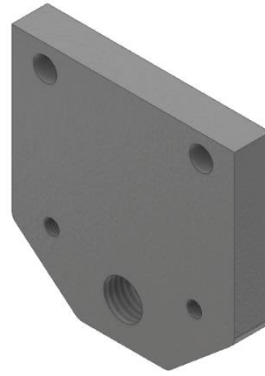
Batente de amortecimento com furo roscado para ligação ao cilindro
